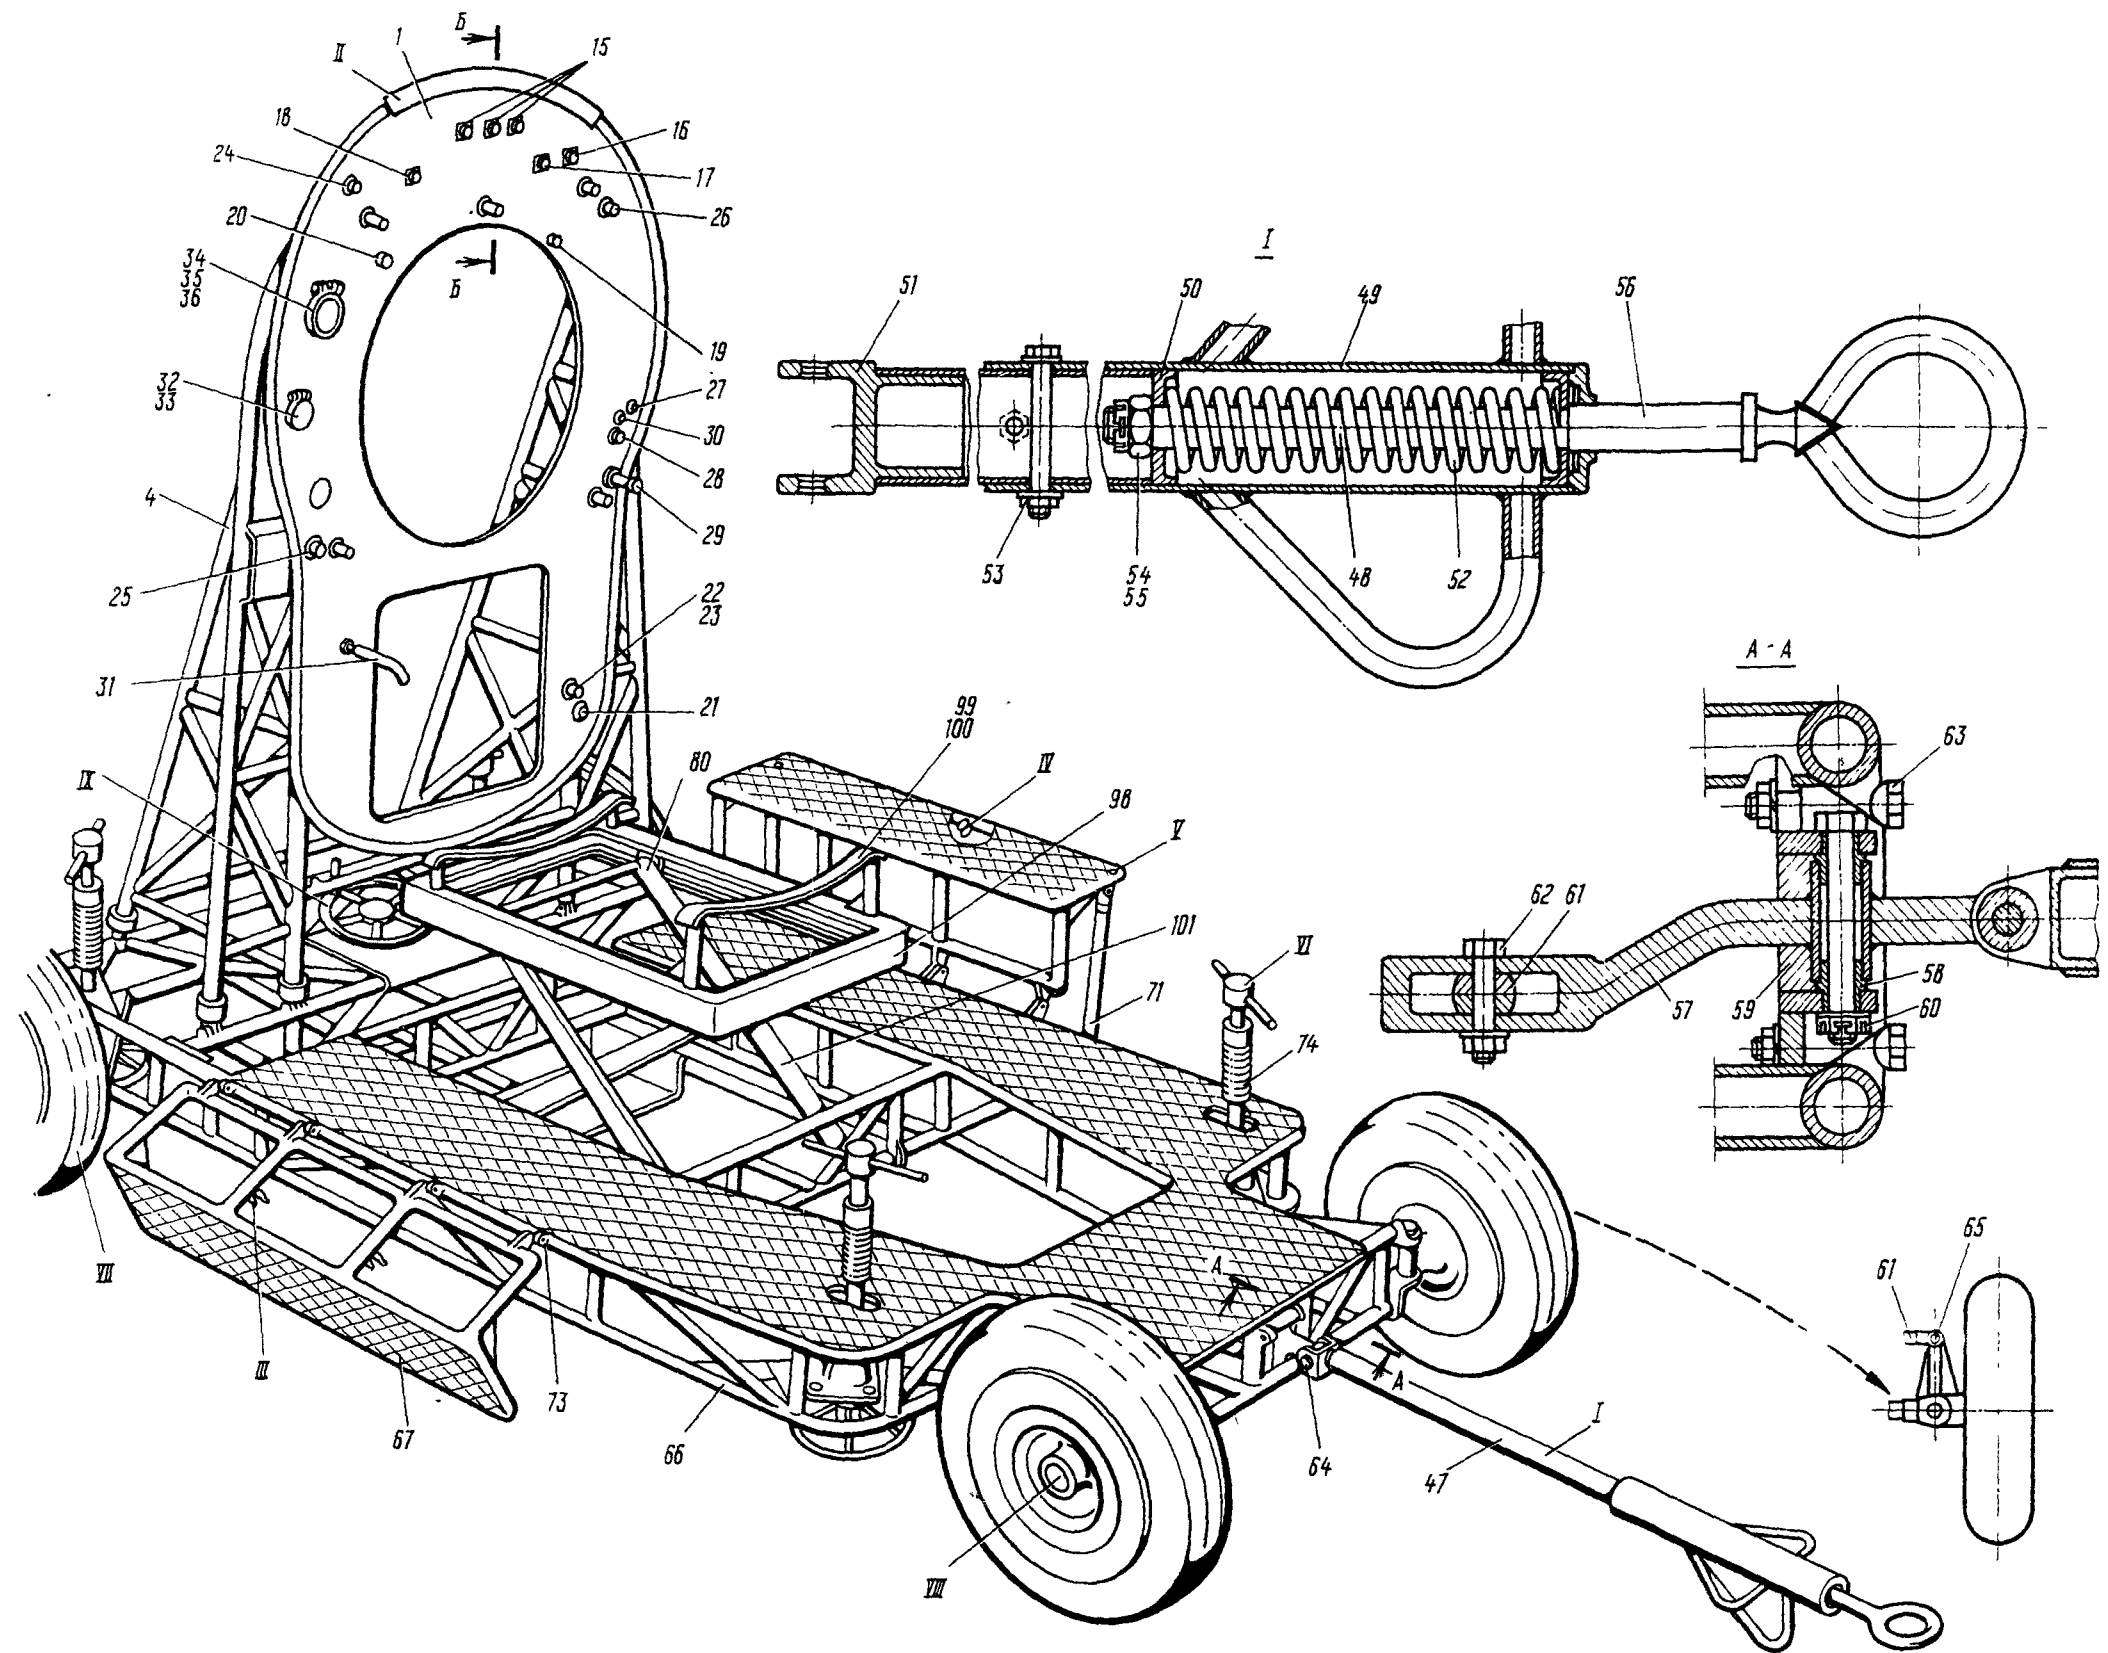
СТЕНД ДЛЯ МОНТАЖА ДВИГАТЕЛЯ (ЛИСТ I)
